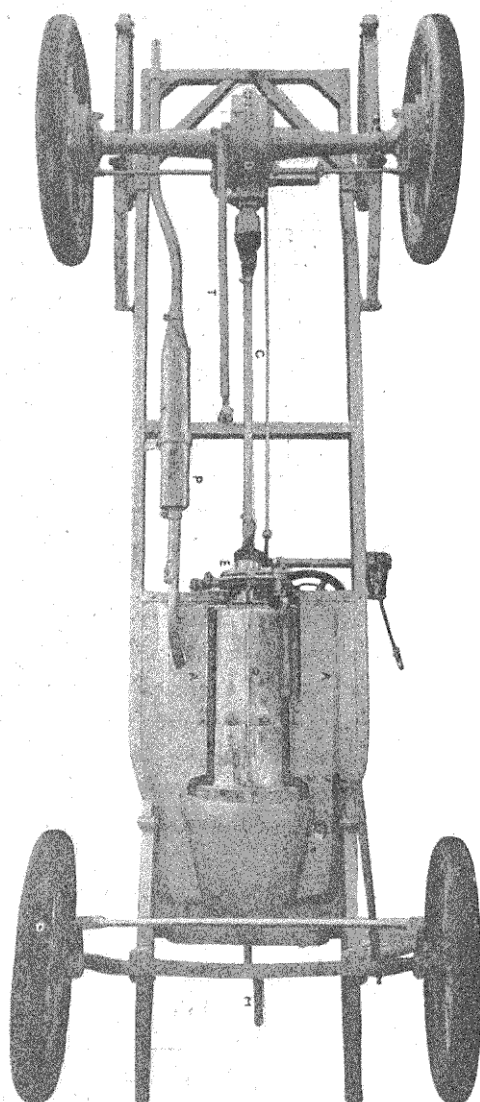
Vue en dessous d'un châssis Motobloc.
